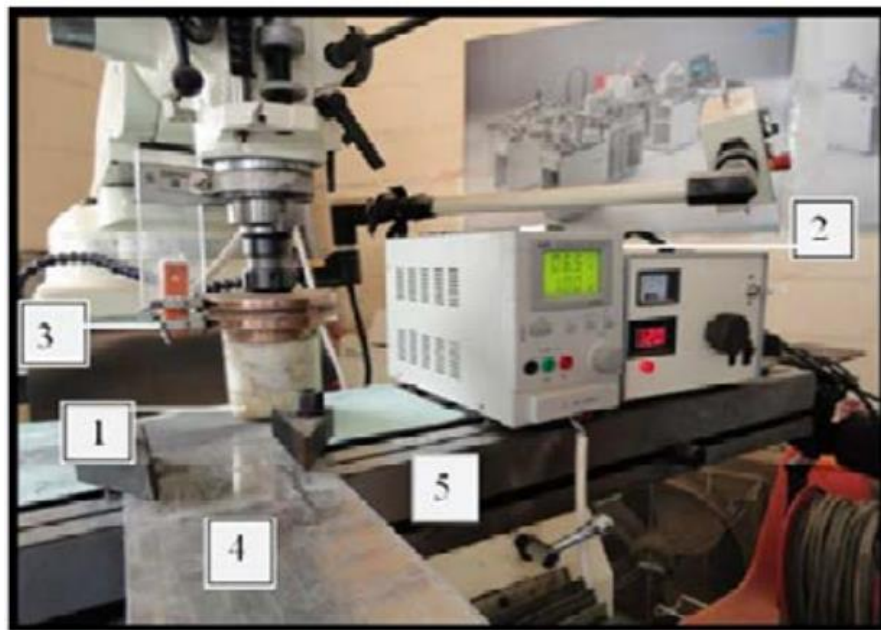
Зображення установки для MAO: 1- індуктор; 2 – блок живлення; 3 – кільця електромагніту; 4 – заготовка; 5 – робочий стіл
